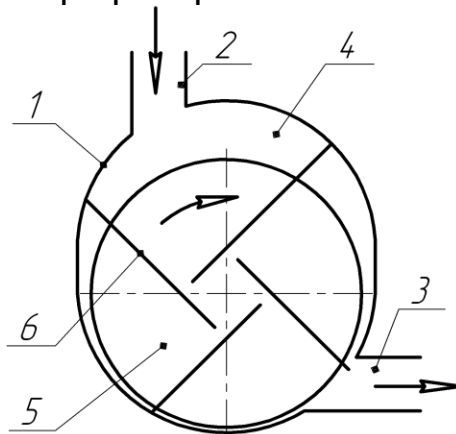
Схема вакуумного насоса з робочою камерою овальної форми: 1 – корпус; 2 – впускний патрубок; 3 – випускний патрубок; 4 – робоча камера; 5 – ротор; 6 – лопатка.
